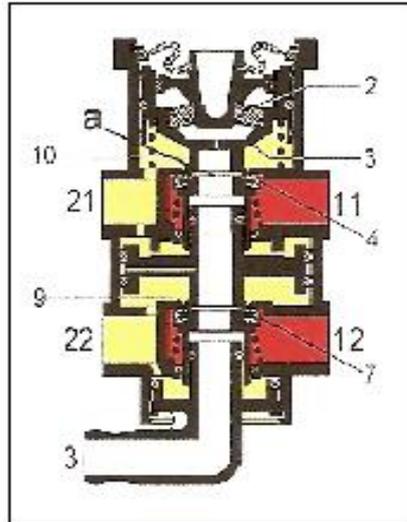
Válvula de pedal. Posición de equilibrio
